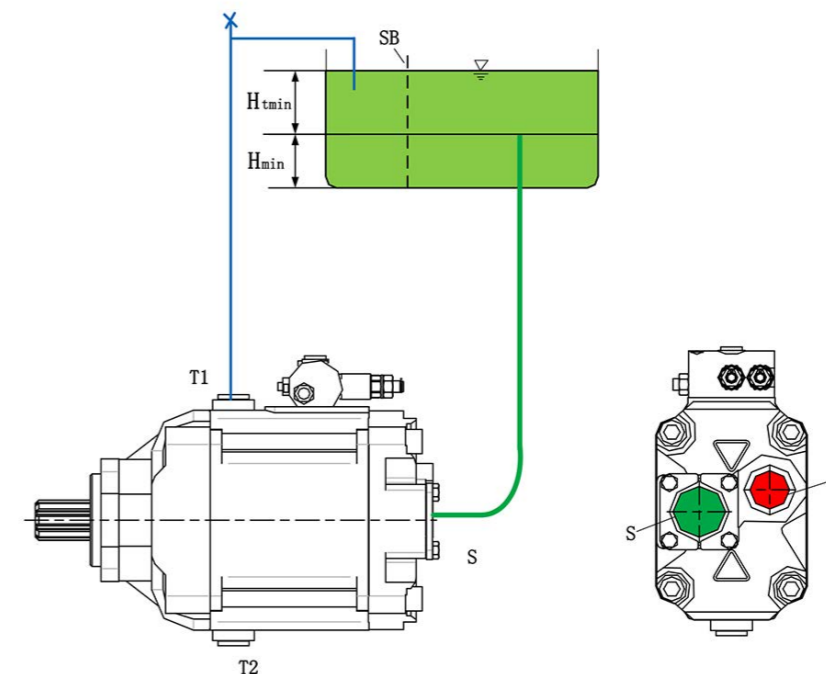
Einbau V60N unter dem Tank (Horizontaler Einbau)
